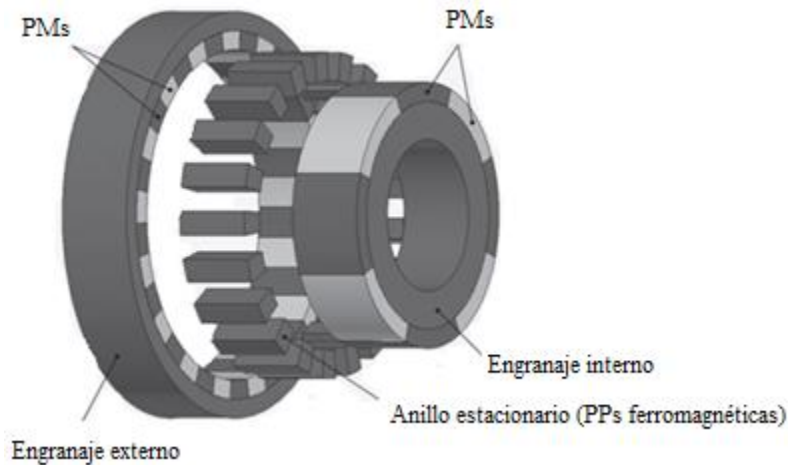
Estructura de los engranajes magnéticos coaxiales.
